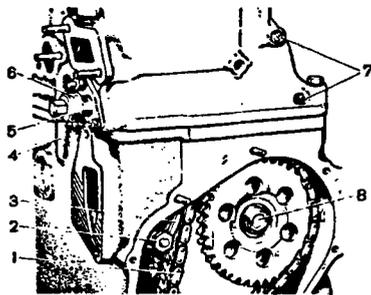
Снятие натяжителя и успокоителя цепи: 1 - цепь привода распределительного вала; 2 - болт крепления башмака; 3 - башмак натяжителя; 4 - гайка крепления натяжителя; 5 - корпус натяжителя; 6 - колпачковая гайка натяжителя; 7 - болты крепления успокоителя; 8 - болт крепления звездочки валика привода масляного насоса
